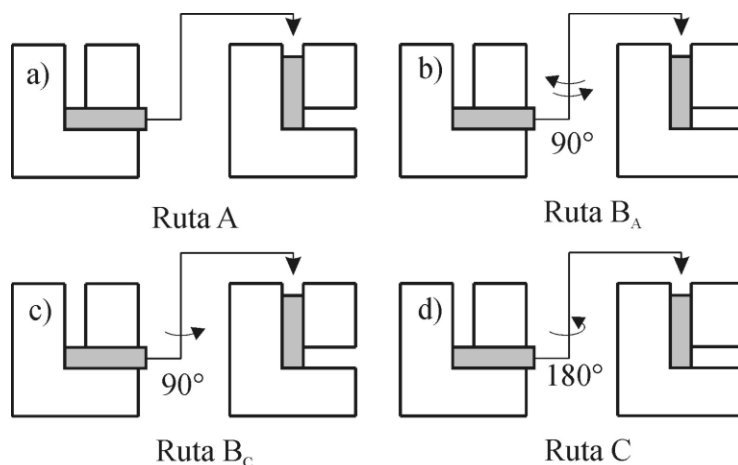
3 Rutas de procesamiento por extrusión en canal angular constante [20].
